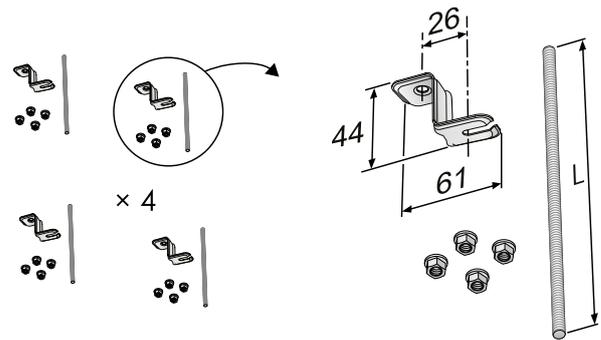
Élément d'assemblage SYST MS M8-1, montage au plafond et sur tige filetée
